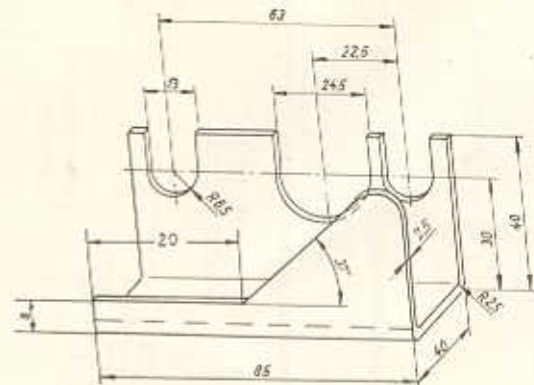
Einstelllehre für Ritzelflansch (Maßskizze)
